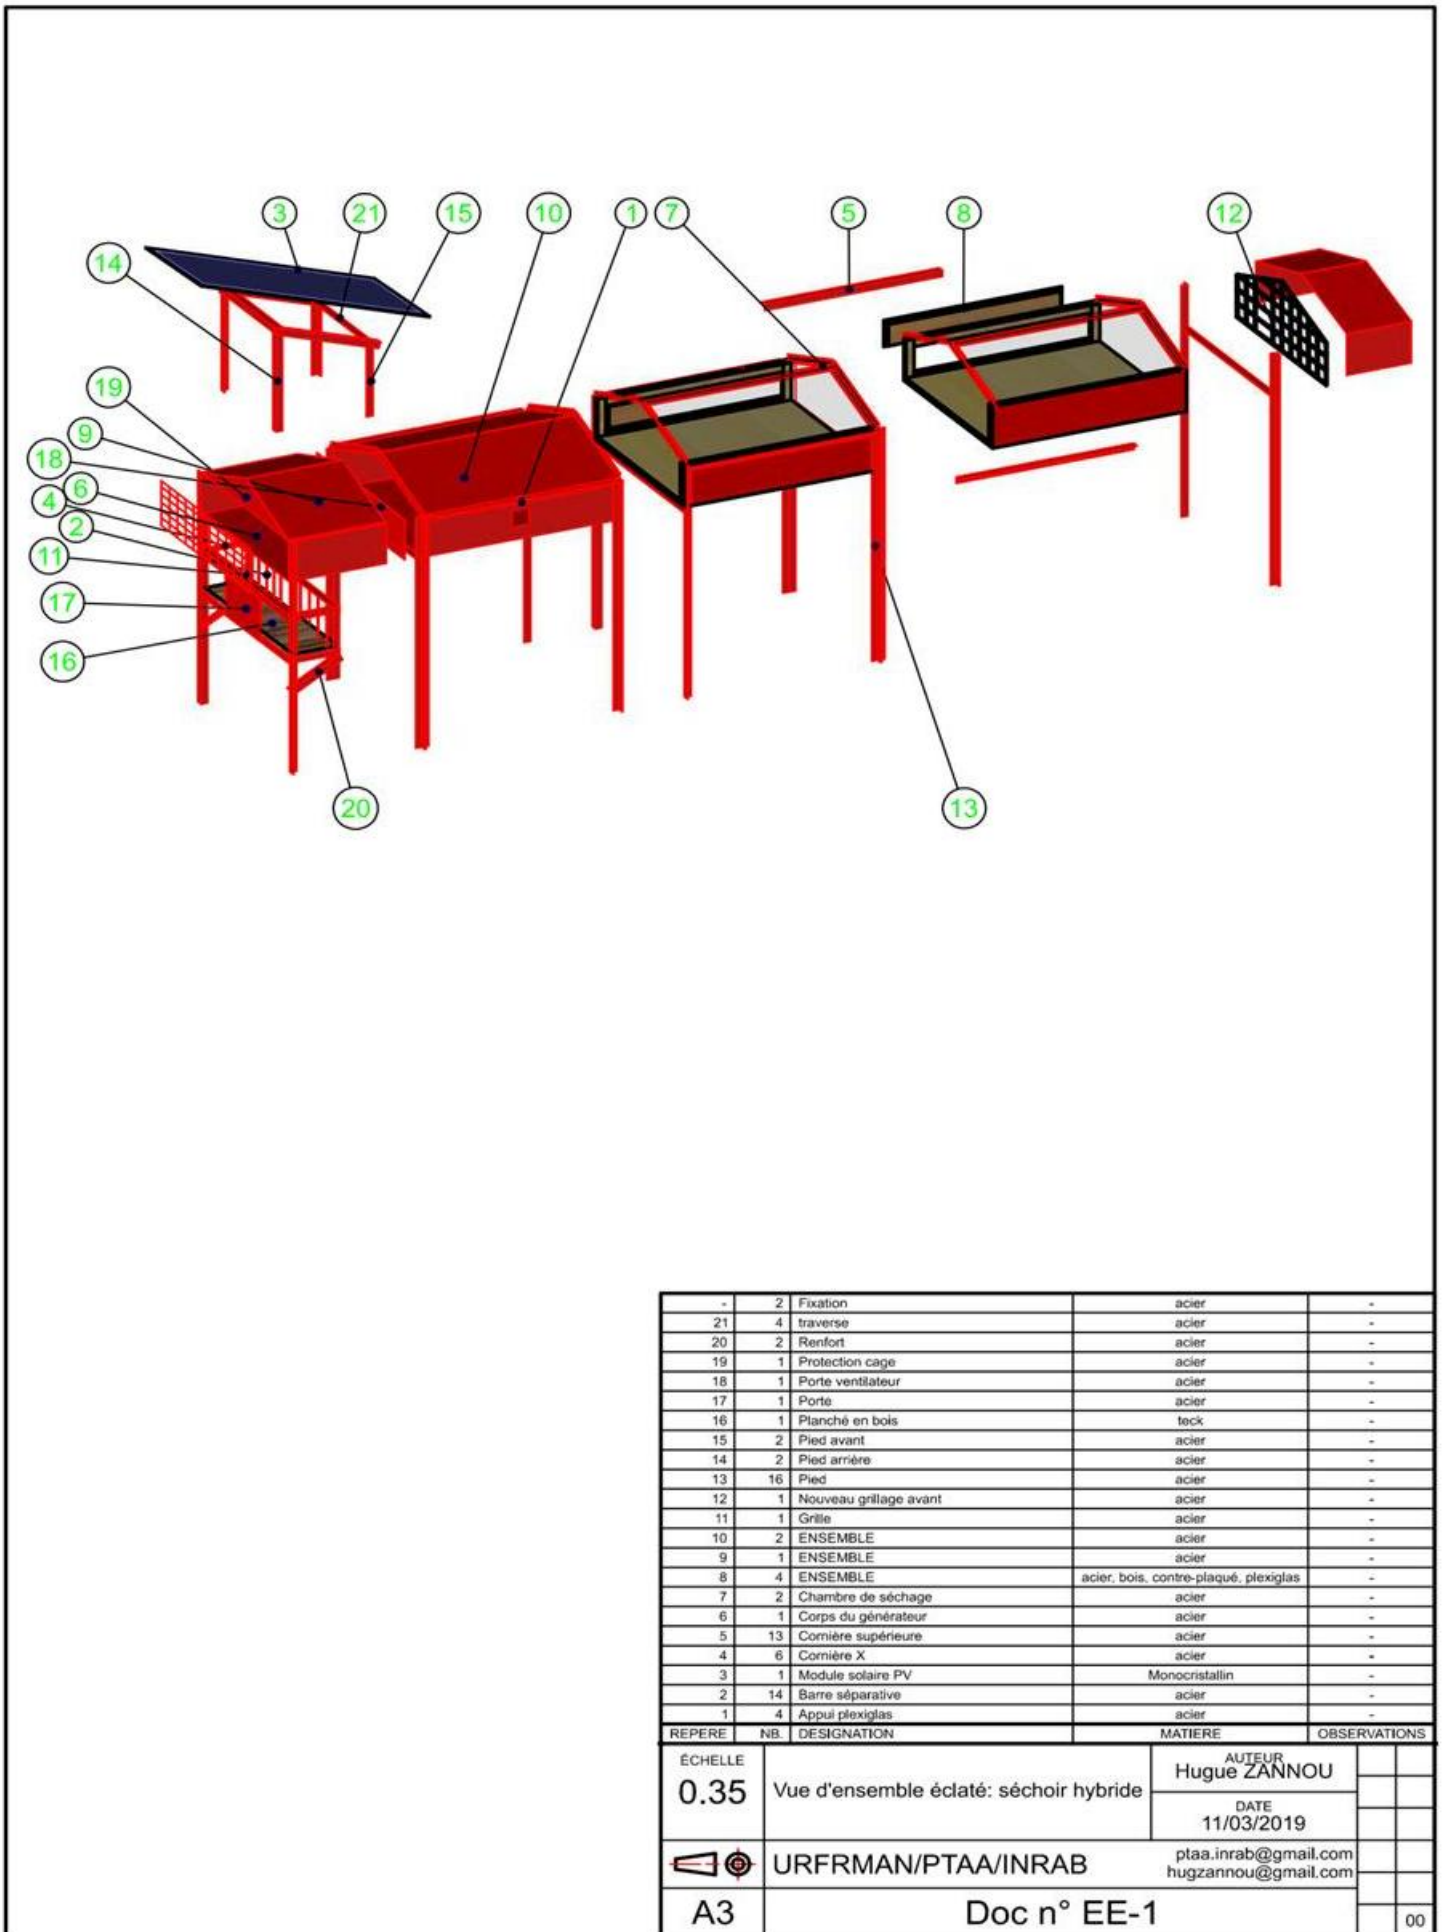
Dessin de la vue éclatée du séchoir solaire hybride
